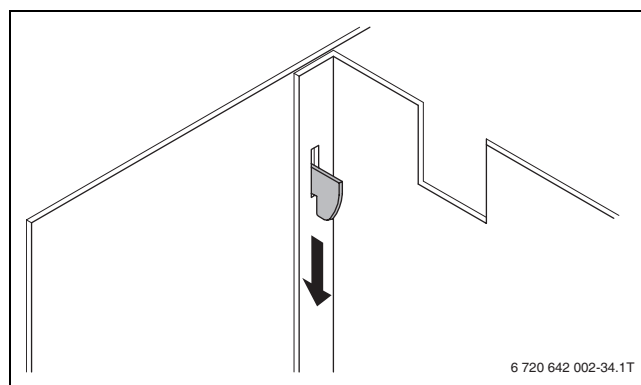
SP161-15: Přehnutí jazýčků přední stěny
